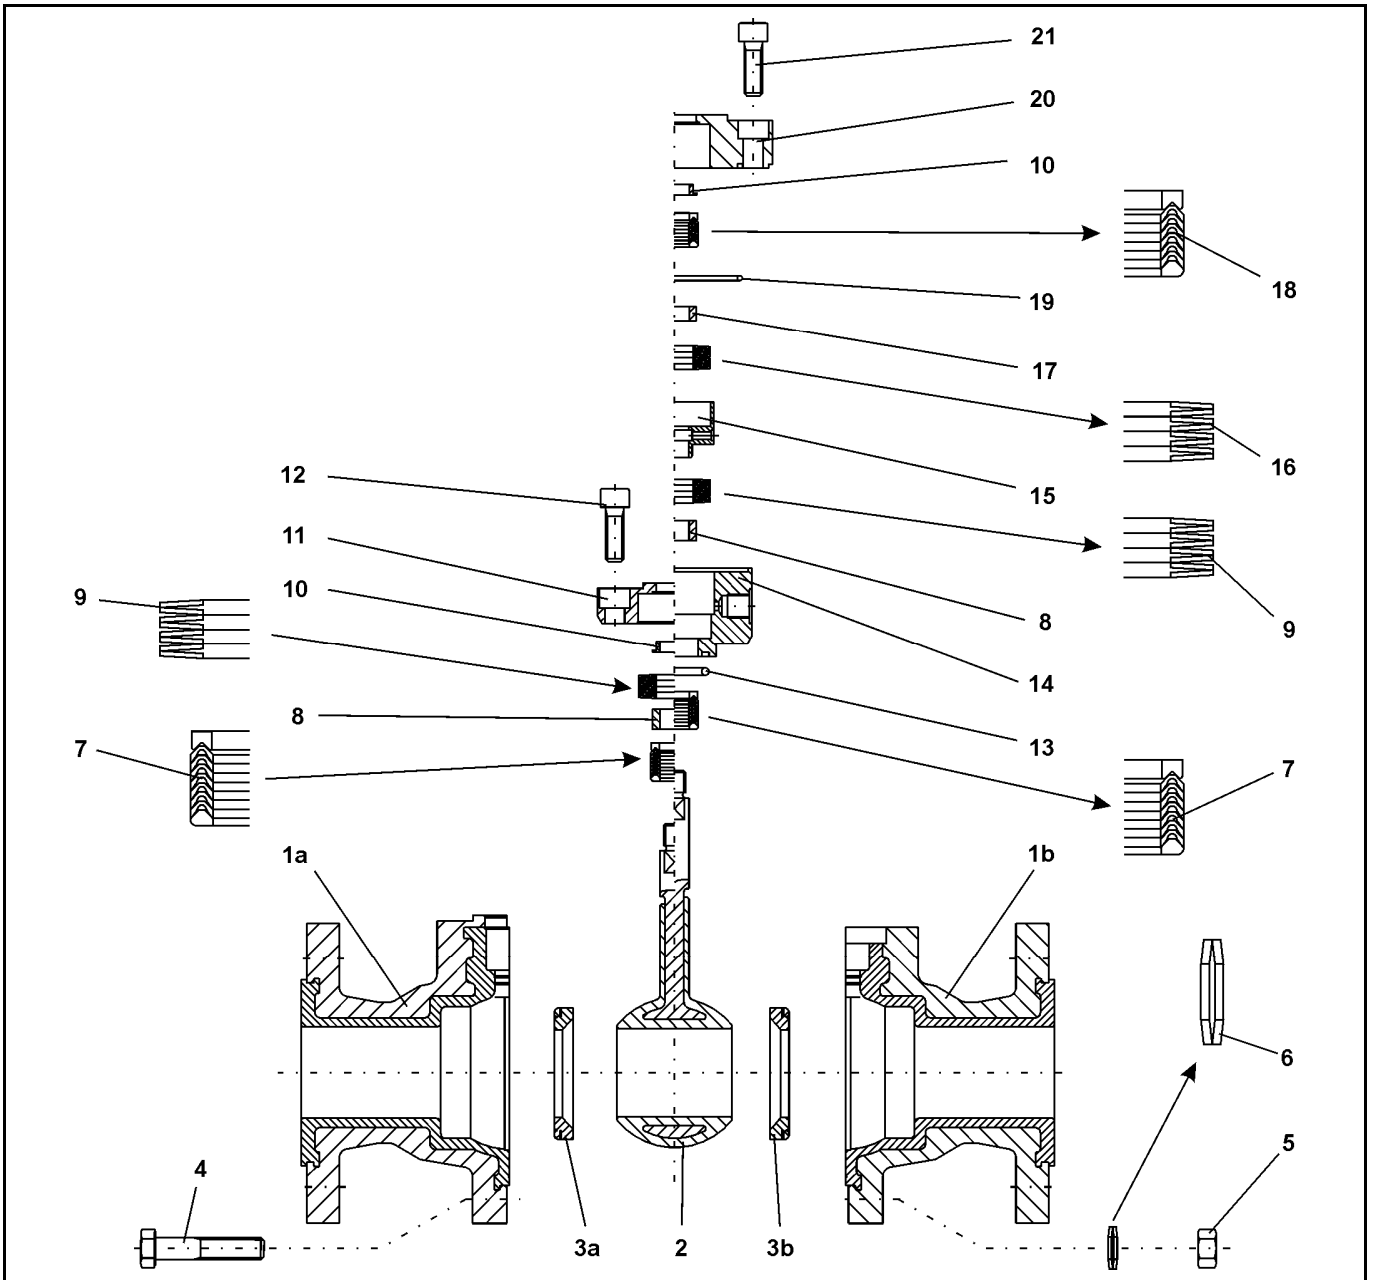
Explosionszeichnung des DIN-Kugelhahns BR 20a
